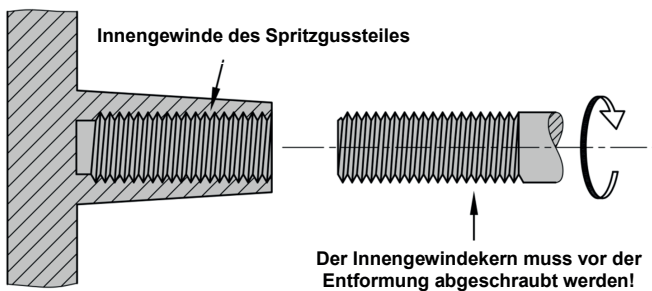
Schema eines Ausschraubmechanismus zur Formung von Innengewinden
